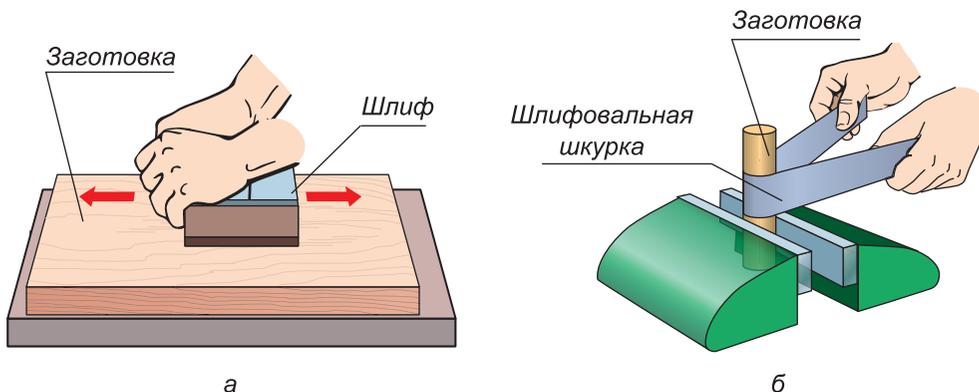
Шлифование: а – плоских заготовок; б – цилиндрических заготовок
